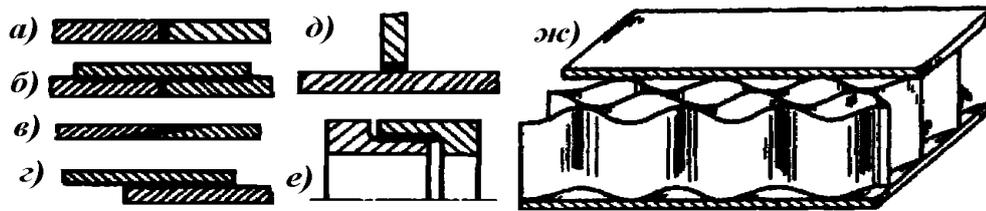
Некоторые типы паяных соединений: а) – встык; б) – встык с накладкой; в) – в косой стык; з) – внахлёстку; д) – втавр; е) – телескопическое; ж) – сотовая конструкция.
